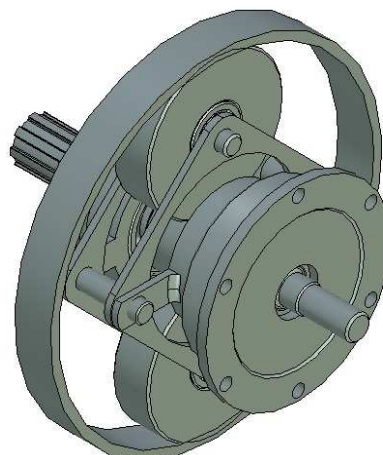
3D-модель двухсателлитного редуктора с видоизмененным водилом
